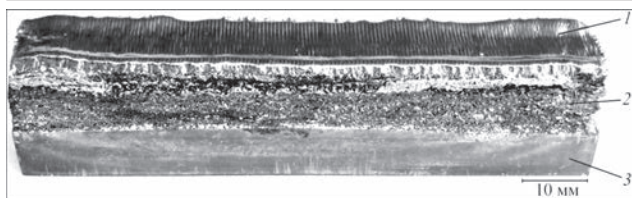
Образец изделия, изготовленный методом электронно-лучевой 3D-наплавки: 1 — верхний слой наплавленного металла; 2 — промежуточный слой металла с частицами несплавленного порошка; 3 — подложка из титана
